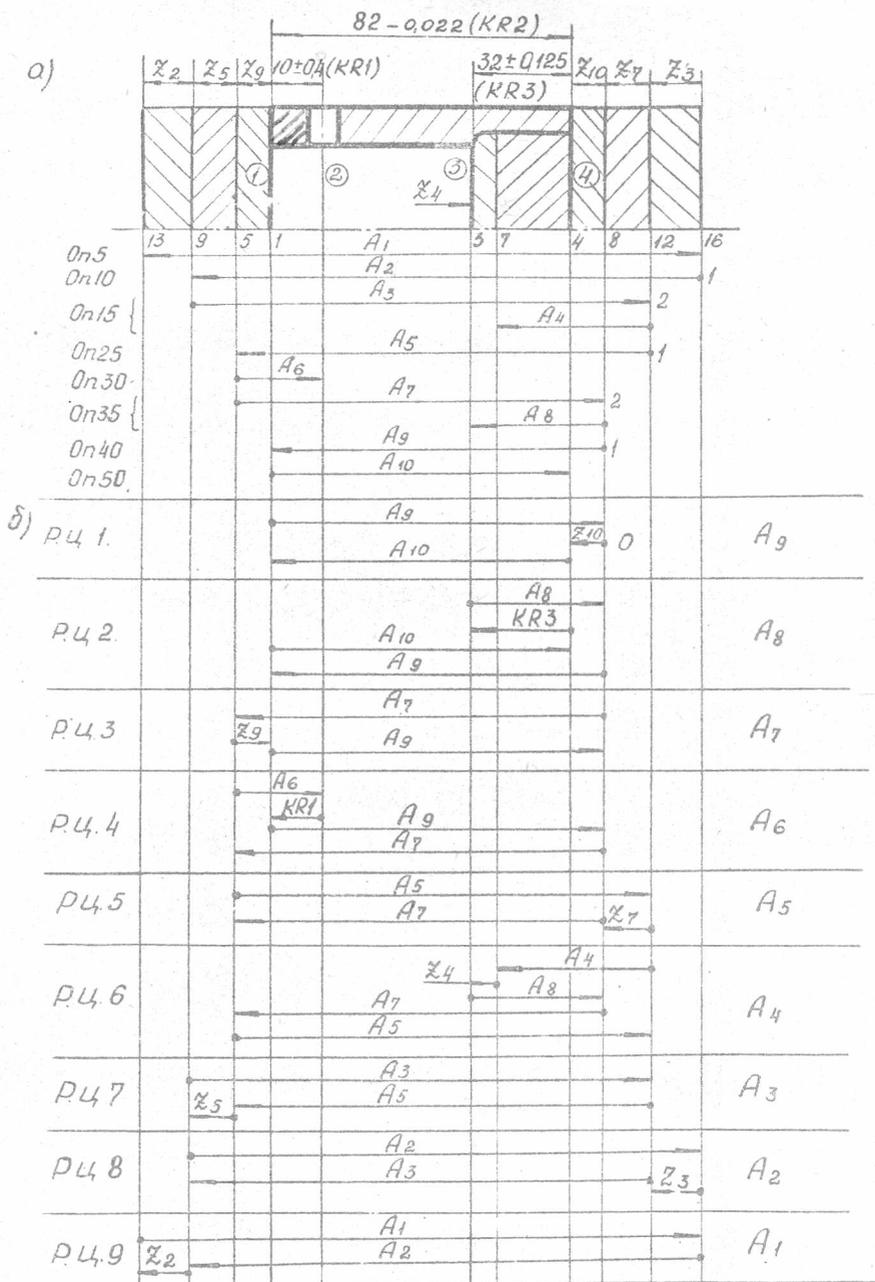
Размерная схема обработки детали (а), размерные цепи (б).
